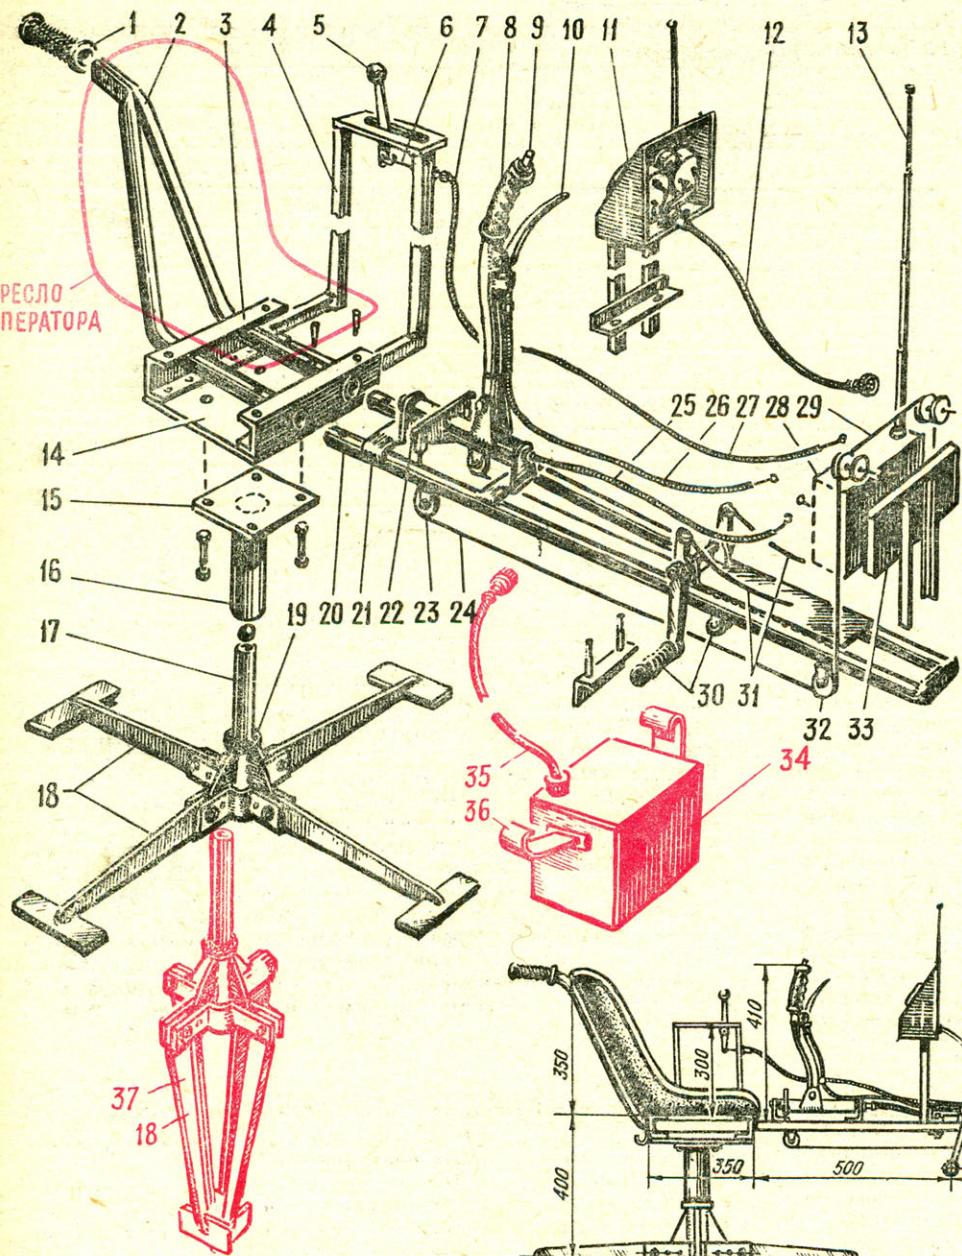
Общая компоновка кресла с преимущественным применением деталей из металла: 1 — резиновая рукоятка поворотного рычага, 2 — труба поворотного рычага, 3 — швейлер основания сиденья оператора, 4 — подрамник сектора газа, 5 — рукоятка сектора газа, 6 — трос управления газом (открытая часть), 7 — трос управления газом (в гибкой оболочке), 8 — ручка управления элеронами и рулём высоты, 9 — кнопка выключения двигателя, 10 — рычаг управления тормозами
